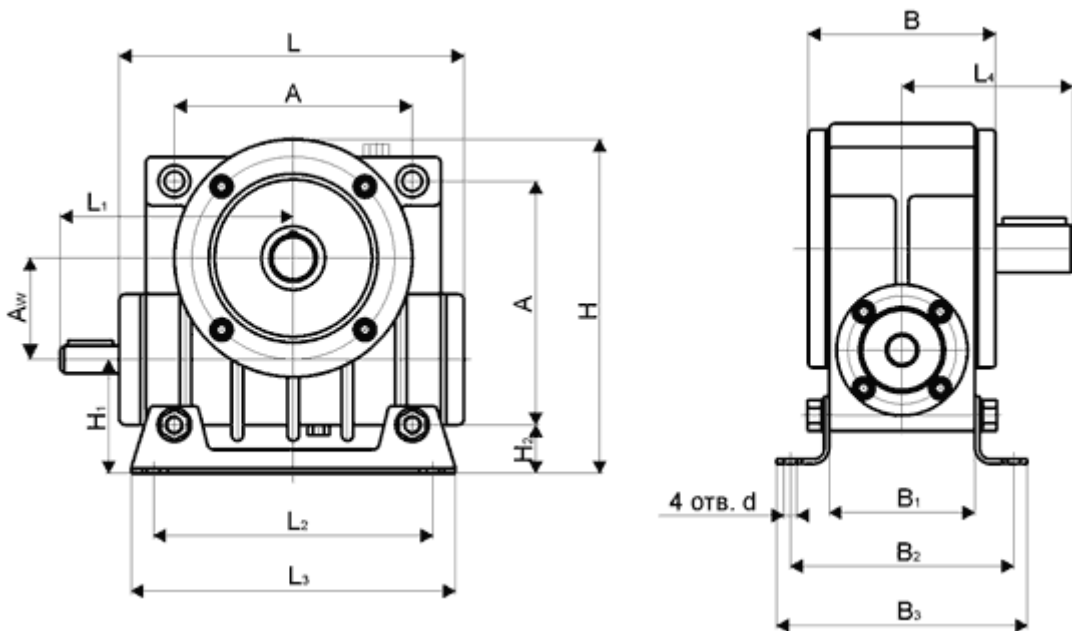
Габаритні і приєднувальні розміри редуктора 2Ч-63
